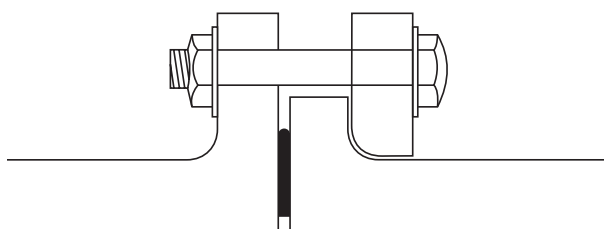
Joint à bride tournante avec joint d'étanchéité plat
